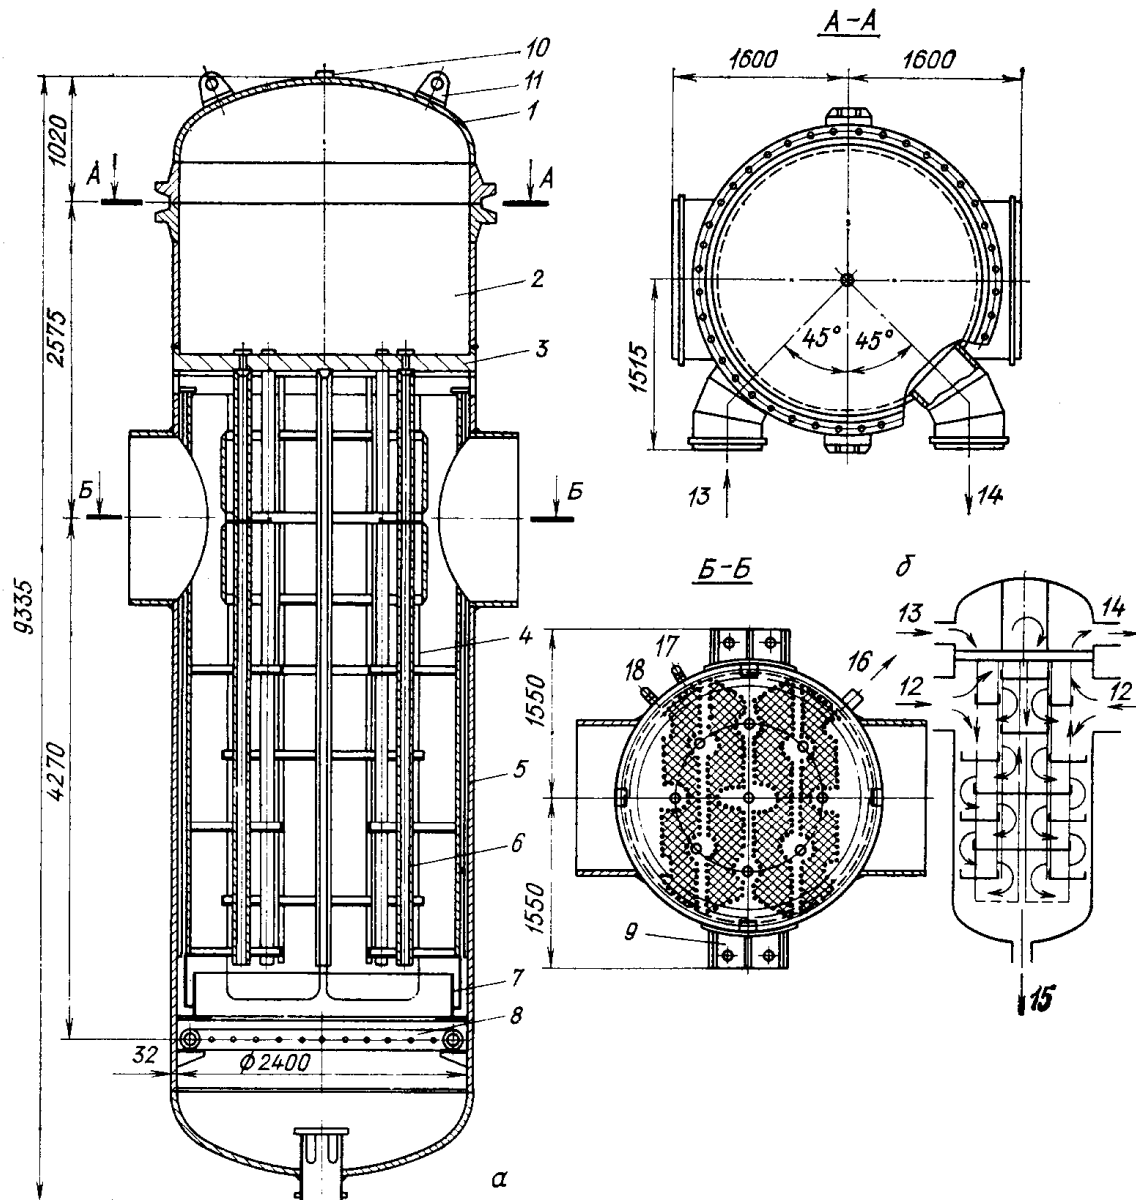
Подогреватель низкого давления ПН-1500-3,2-0,6:
